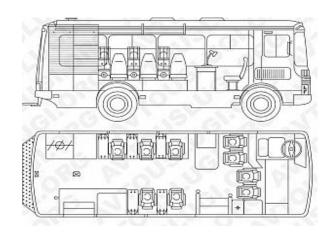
Схема аварийно-спасательного автобуса ПАЗ 32053.
